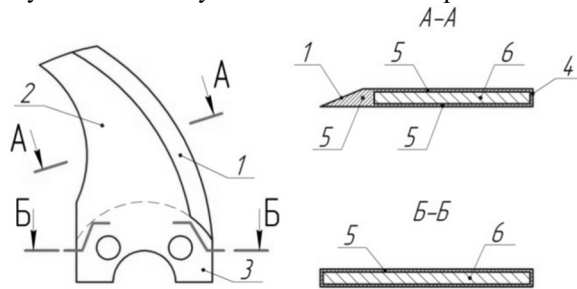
Схема зміцнення ножа кутера: 1 - лезо ножа; 2 - робоча частина; 3 - посадкова частина; 4 - тильна сторона; 5 - зміцнений шар підвищеної твердості; 6 - нормалізований або покращений шар зниженої твердості.
